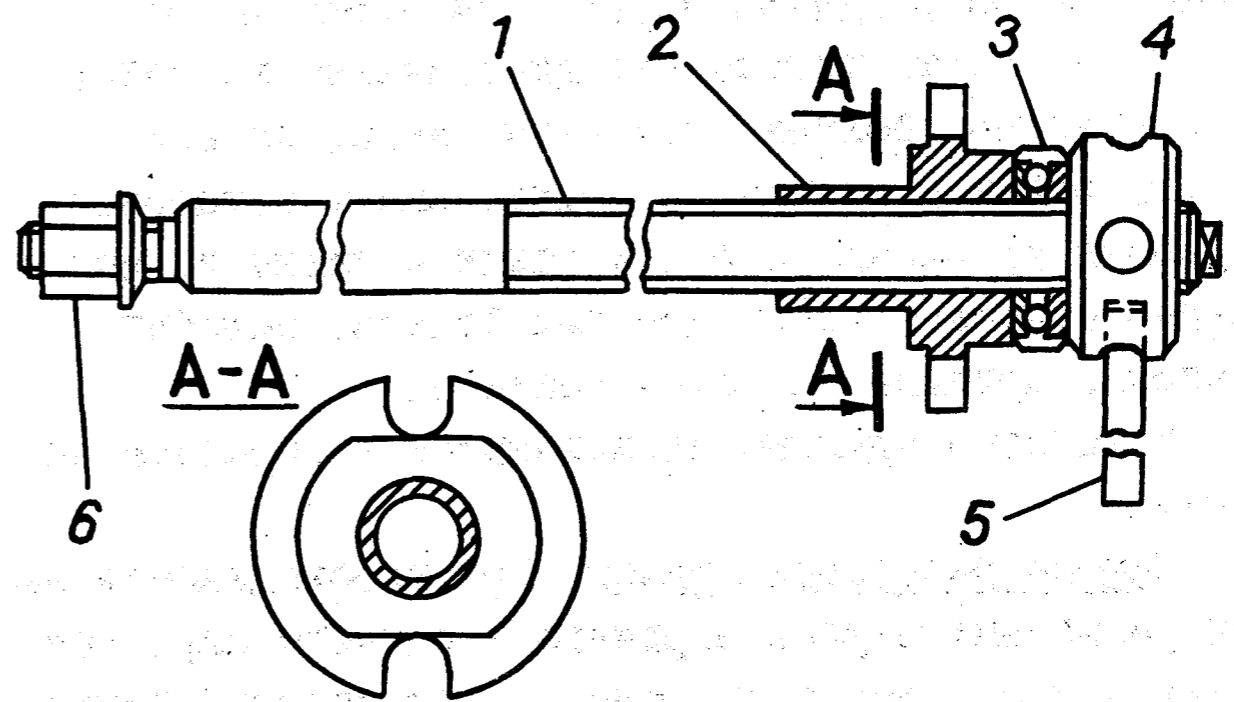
Приспособление 7823-6709 для сжатия пружины подвески:
